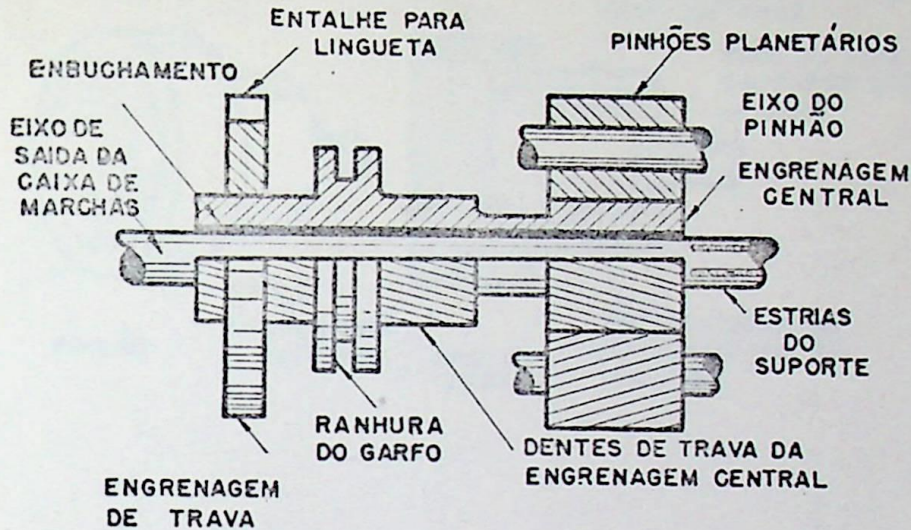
Conjunto da engrenagem central. Engrenagem central engrenando com os pinhões. Engrenagem de trava é estriada na engrenagem central. O conjunto pode girar em torno do eixo de saída da caixa de marchas quando desejado. Os pinhões planetários fazem parte do conjunto de suporte de pinhões.
